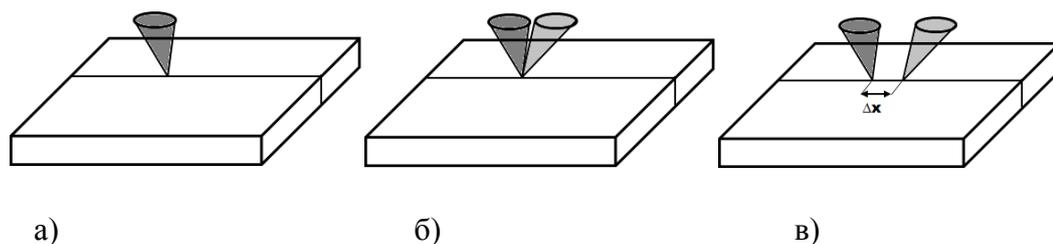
Различные способы лазерной сварки: а) однолучевая сварка;
